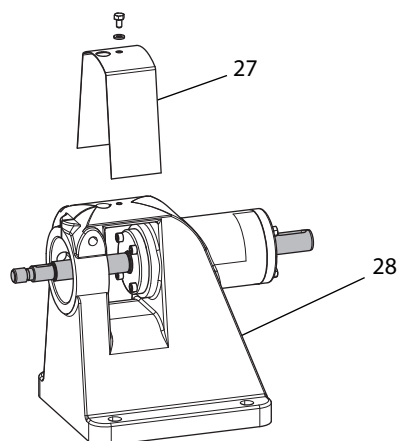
Extracción de la cubierta del apoyo del rodamiento
